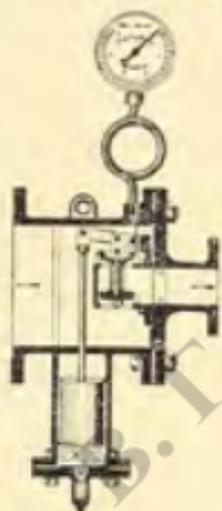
Паровой редукционный клапан. Разгрузка поршневым клапаном. Давление воспринимается поршнем. Установка величины противодавления рычагом и грузом.
